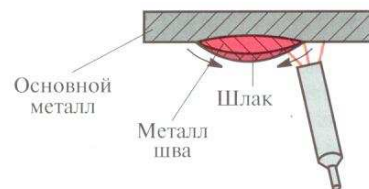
Наплавка способом «сварка по шлаку», выполняемая при наличии тонкого слоя шлака
